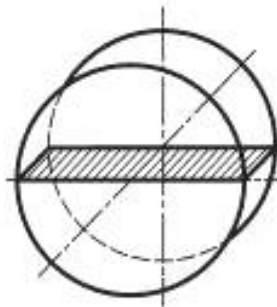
Образец от прутка диаметром не более 25 мм
